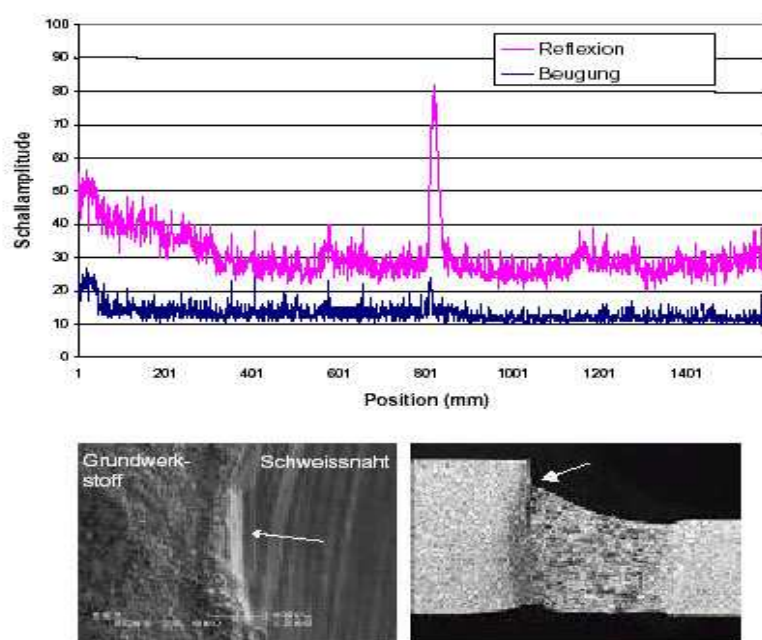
Anzeige eines Flankenbindefehlers in einer Laserschweißnaht [35]
